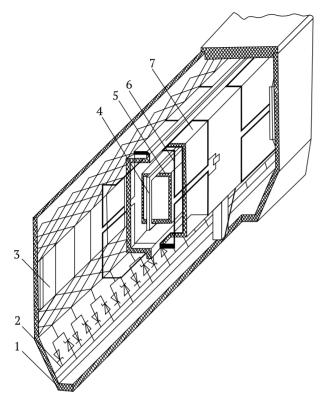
Компоновочная схема ОТС с предлагаемой ТЛС:
